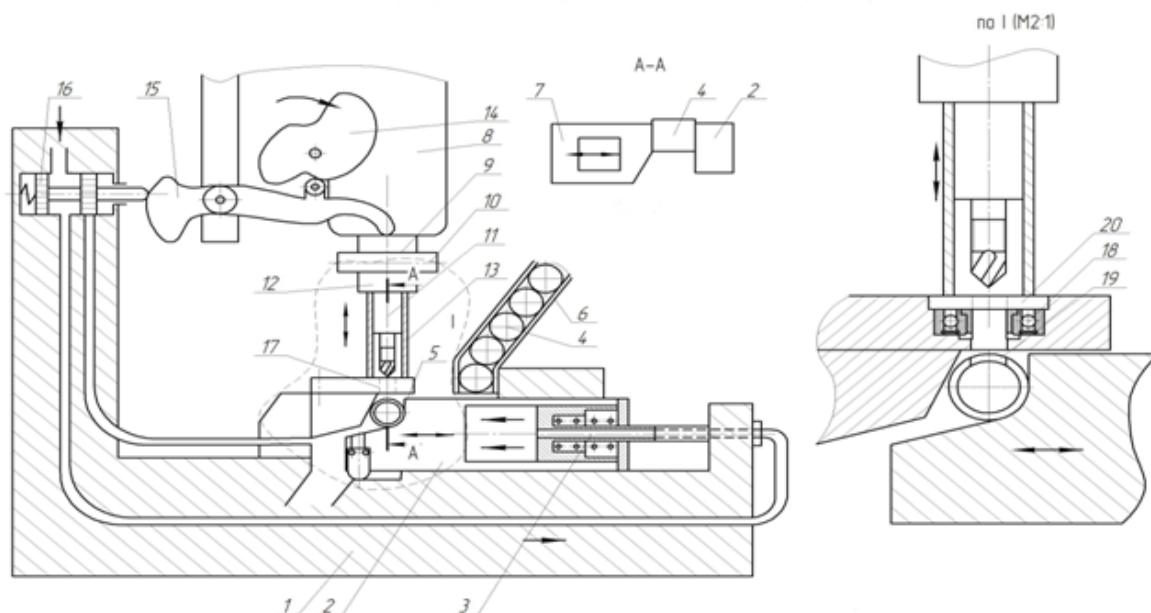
Пневматичний автоматизований пристрій для свердління і нарізання різьби в трубчастих заготовках
